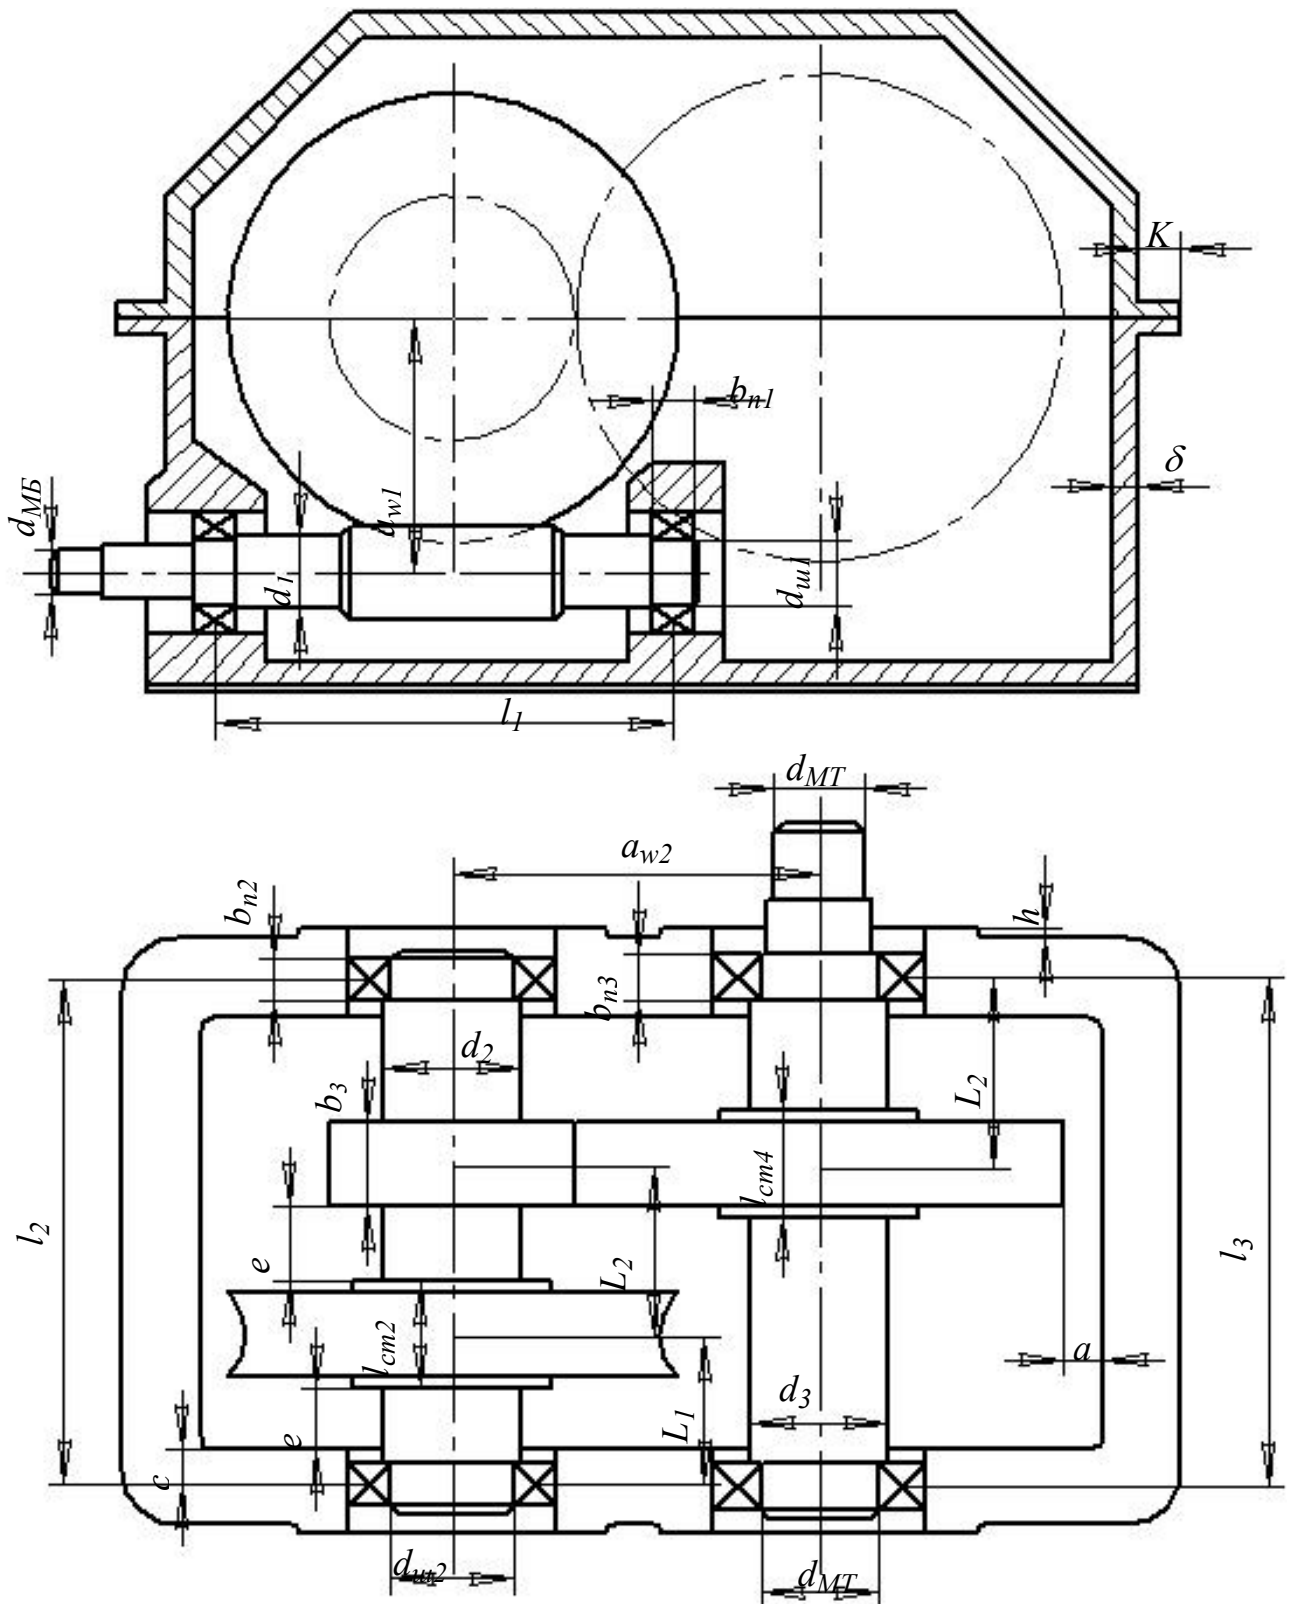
Ескізне компоновання черв'ячно-циліндричного двоступеневого редуктора з нижнім розташуванням черв'яка
